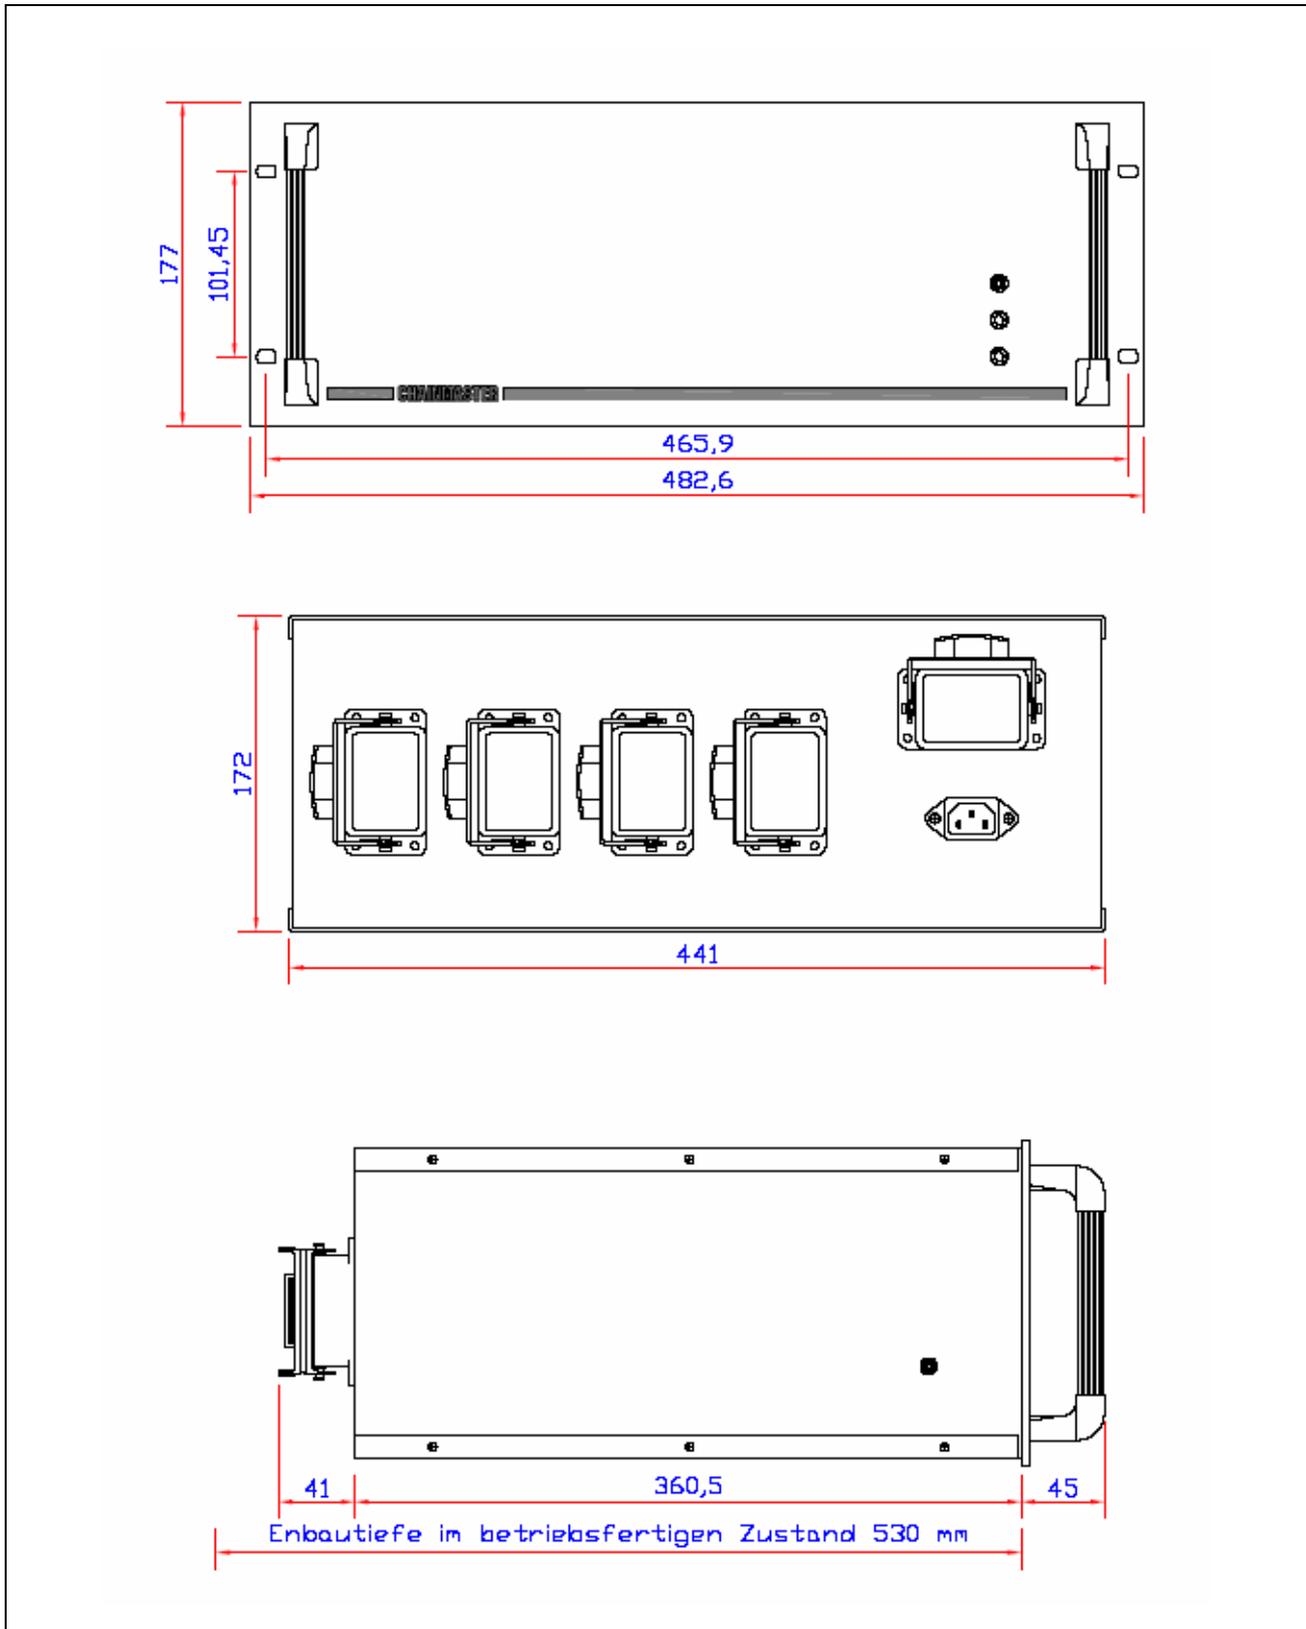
Einbaumaße 4-Kanal Handsteuerung
